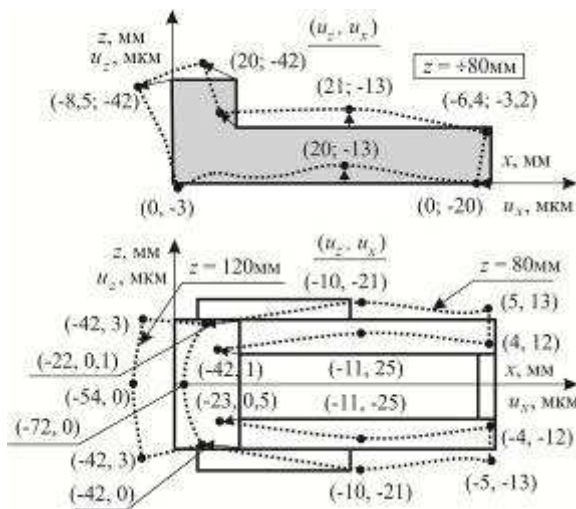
Схема деформування корпусу лещат МДВ 7202.4006
